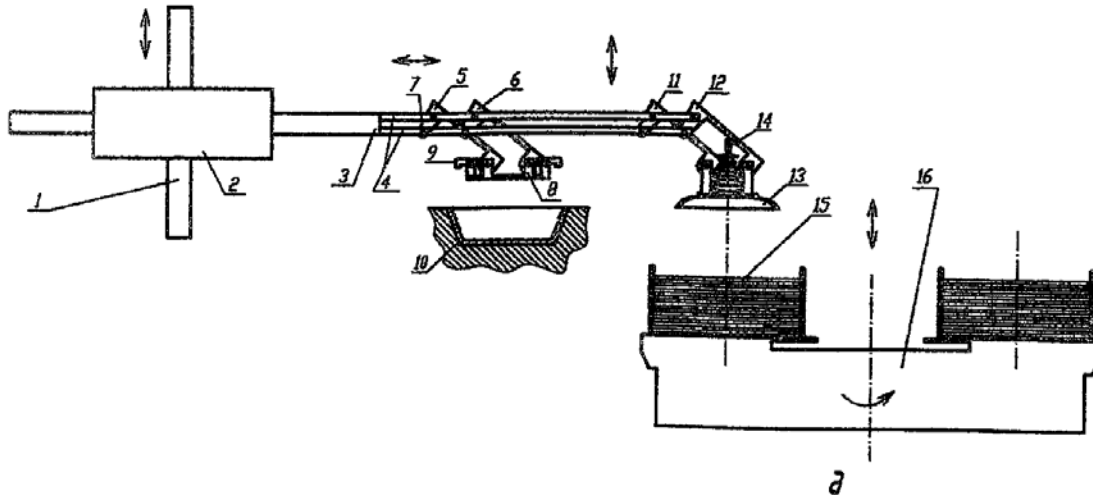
Устройство для подачи плоских заготовок в область штампа
